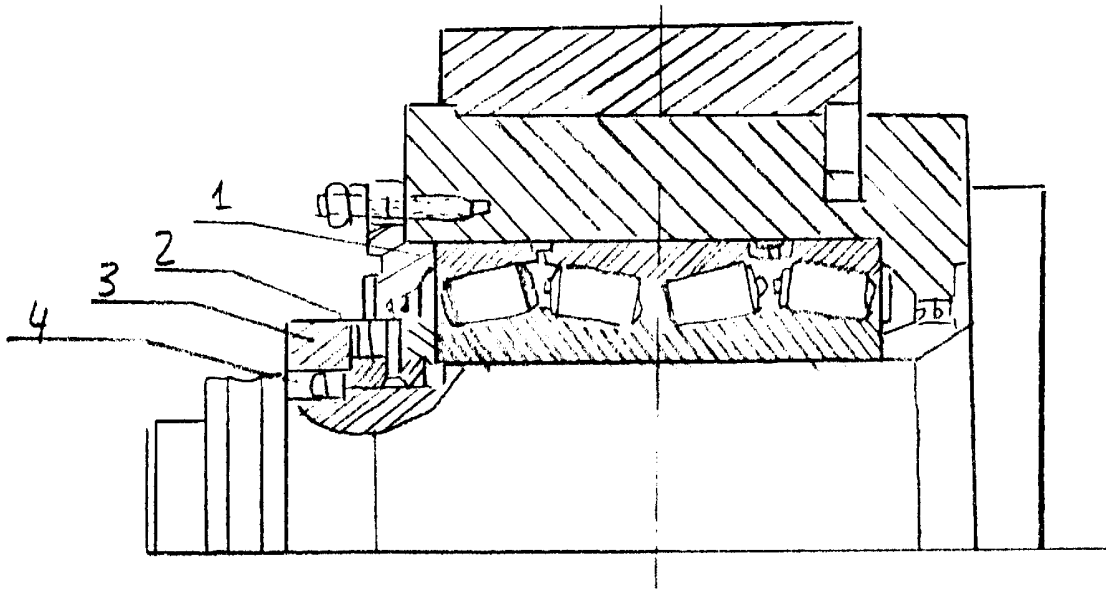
Установка опорного валка на роликових конічних підшипниках
